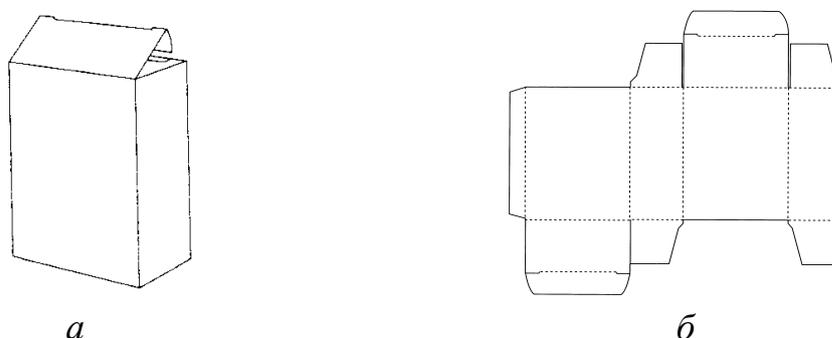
Внешний вид (а) и развертка (б) коробки с реверсной заправкой торцов
